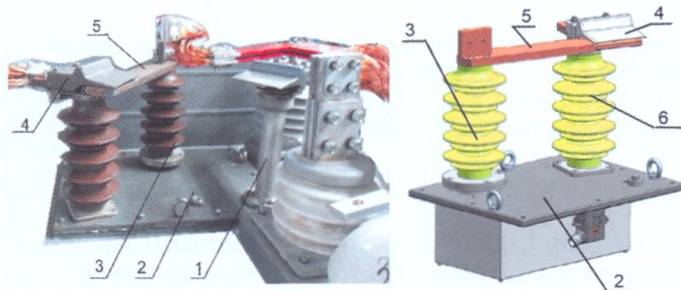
Крышное оборудование — разъединитель-заземлитель OSAD30 (слева) и разъединитель 1OSAD26 (справа):
